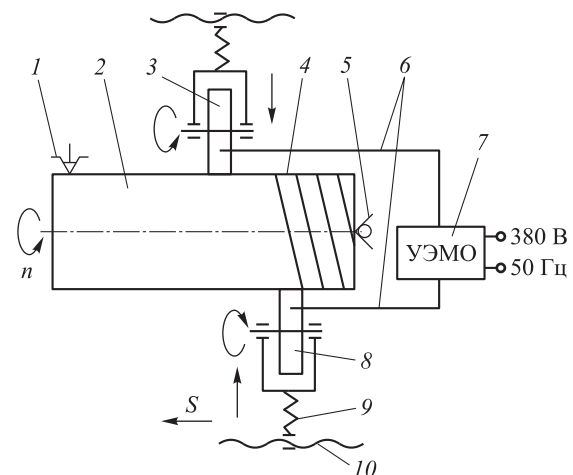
Принципиальная схема ЭМПЗ заготовки на токарно-винторезном станке:
